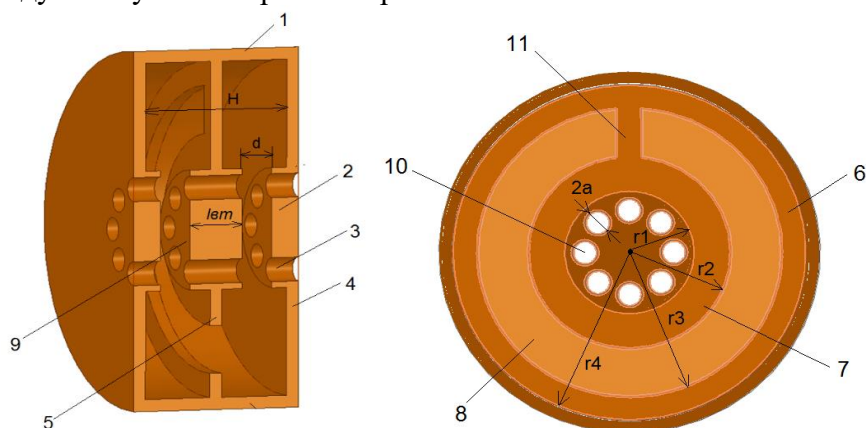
Конструкция двухзачорного резонатора с метаматериалом
